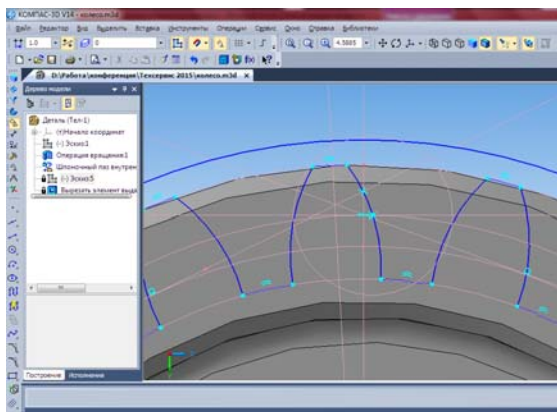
Эскиз эвольвенты зубчатого колеса
